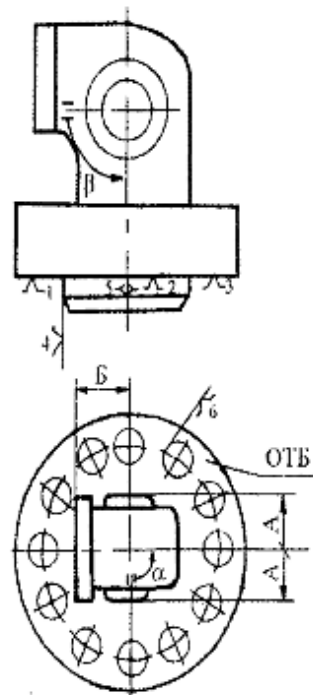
Теоретична схема базування корпусної деталі на плоску поверхню, циліндричний борт і отвір на фланці
